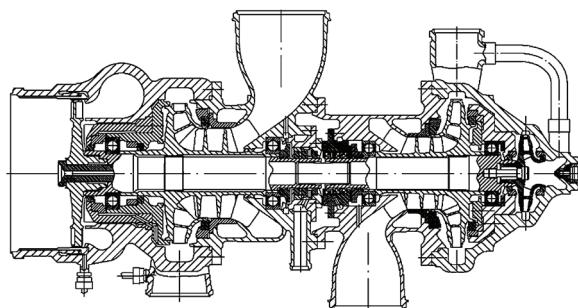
Конструктивная схема ТНА двигателя РД0155
